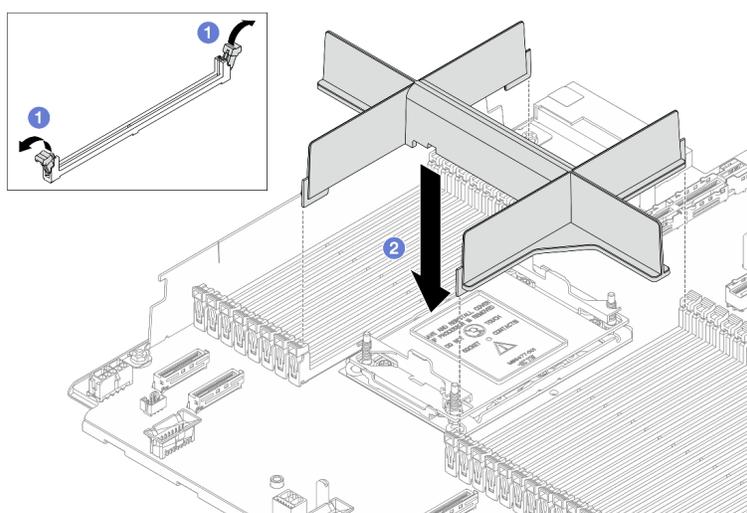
Installation d'un obturateur de module de processeur-dissipateur thermique
